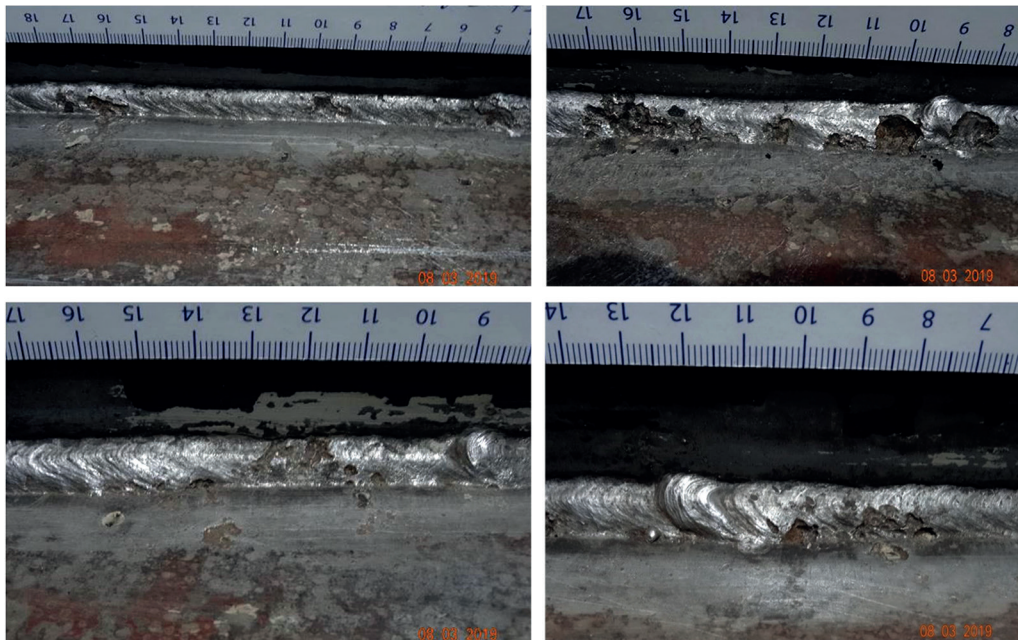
Загальний вид корозійних пошкоджень зварних з'єднань днища
